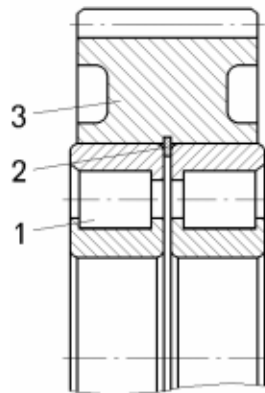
Сателлит первого ряда редуктора 75216:
